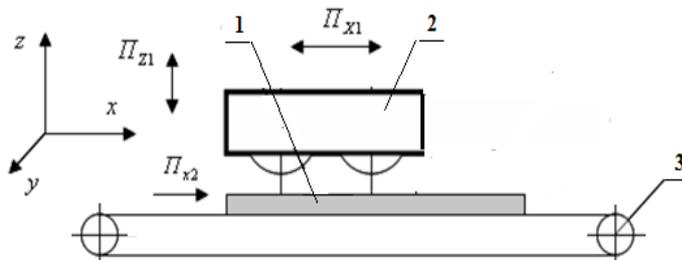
Схема координатных движений исполнительных элементов модифицированной раскатывающей машины: 1 – раскатываемый пласт теста, 2 – каретка с раскатывающими валками, 3 – несущий ленточный транспортер, P_{x1} – возвратно-поступательное движение каретки с валками по оси Ox ; P_{x2} – прямолинейное движение ленты транспортера по оси Ox ; P_{z1} – прямолинейное движение каретки по оси Oz
